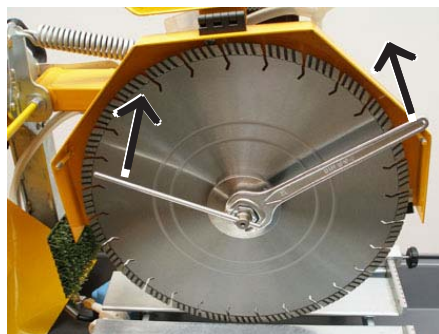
, Затягивание прижимного фланца с гайкой режущего вала к диску
